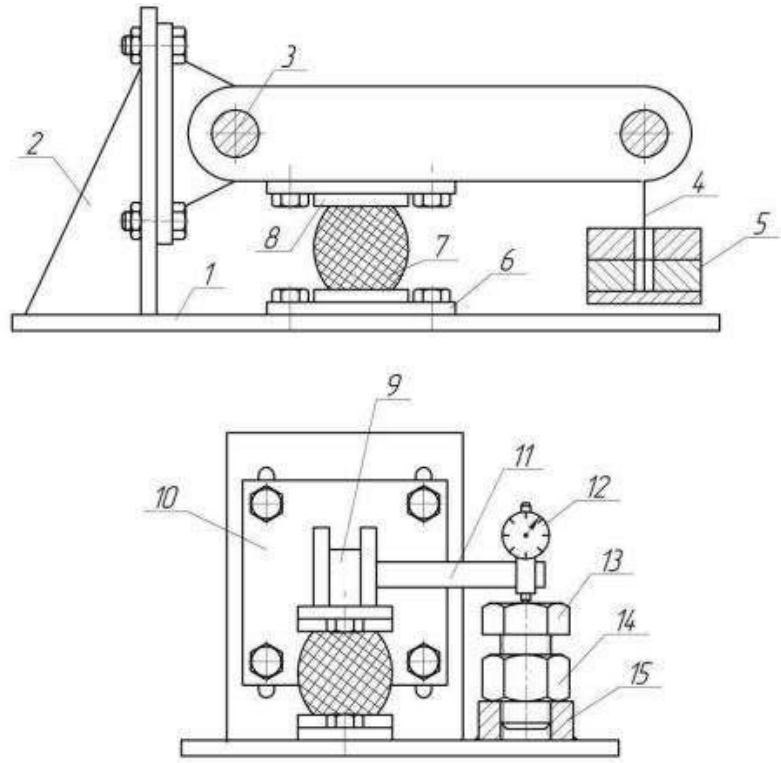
Нагружающее устройство: 1 — основание; 2 — стойка; 3 — ось; 4 — подвес; 5 — груз; 6 — нижняя плита; 7 — образец; 8 — верхняя плита; 9 — рычаг; 10 — кронштейн; 11 — кронштейн индикатора; 12 — индикатор; 13 — винт; 14 — контргайка; 15 — бобышка
